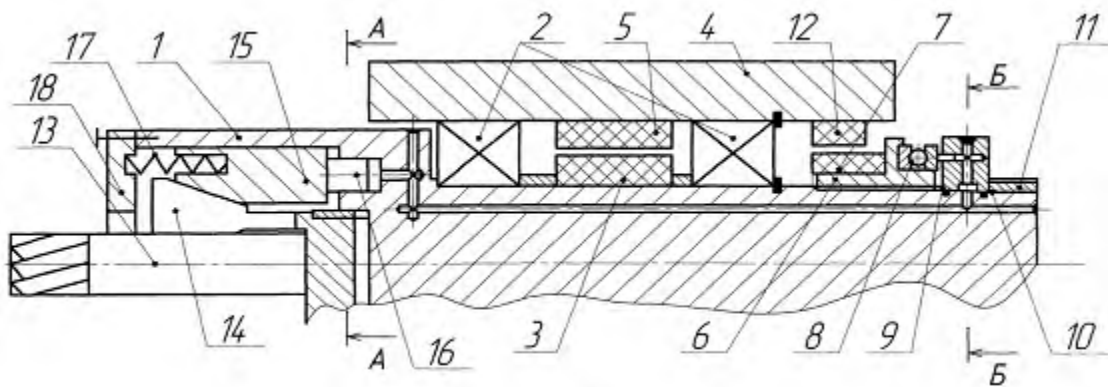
Шпиндельний вузол металорізального верстата [16]
